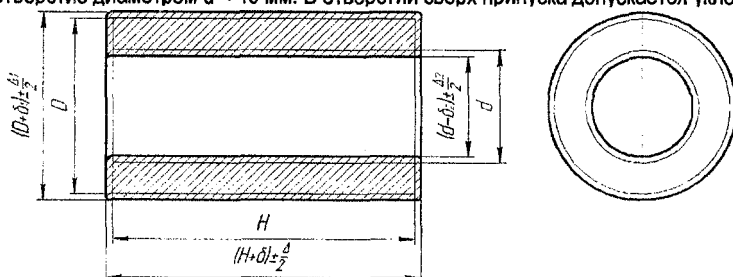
Схема назначения припусков для поковок 4-ой группы
